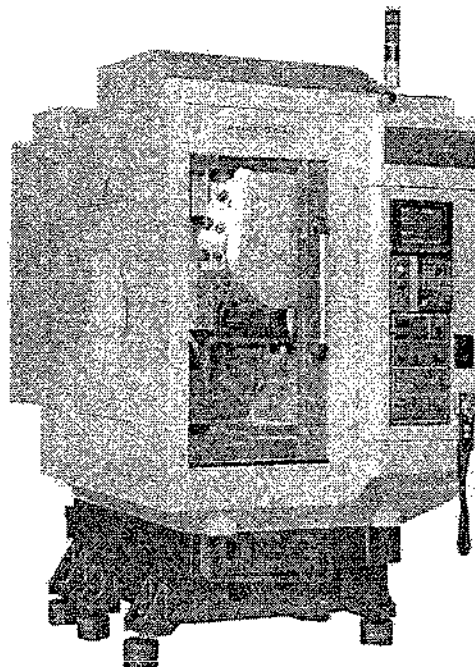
Вертикальный сверлильно – фрезерный центр с ЧПУ Akira Seiki PC 460
